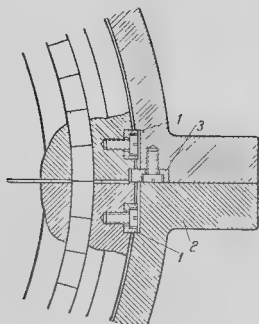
Схема закрепления диафрагмы в корпусе турбины
